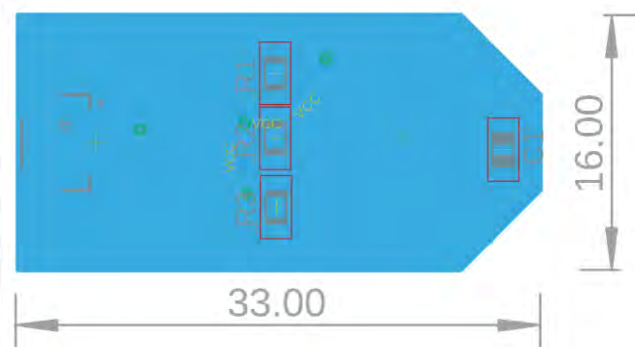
Vista de la base de la tarjeta PCB del bloque de temperatura
